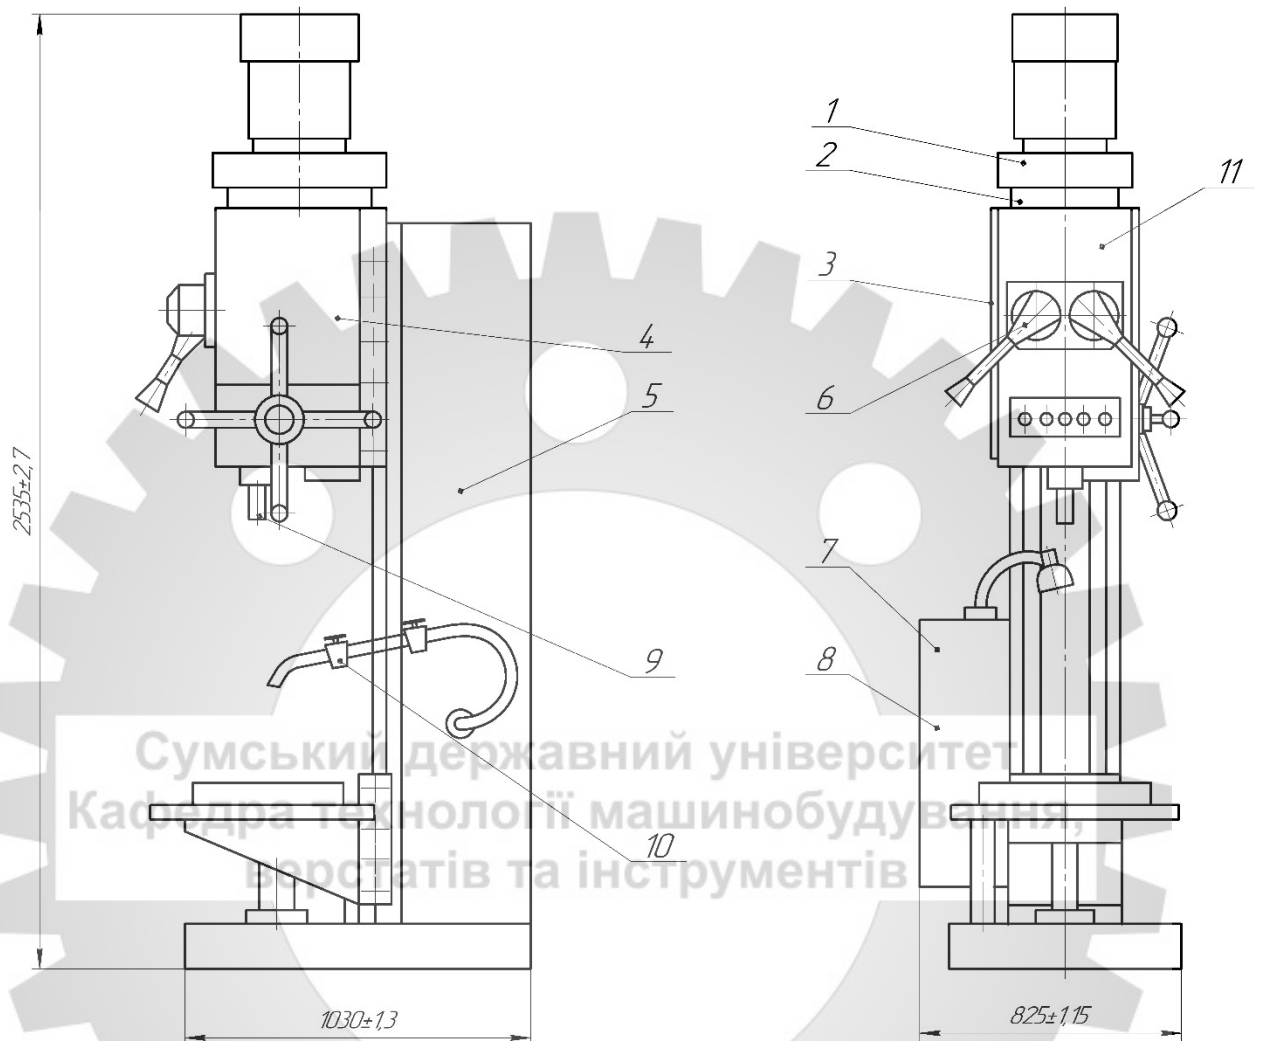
Загальний вид базової моделі верстата 2Н135
